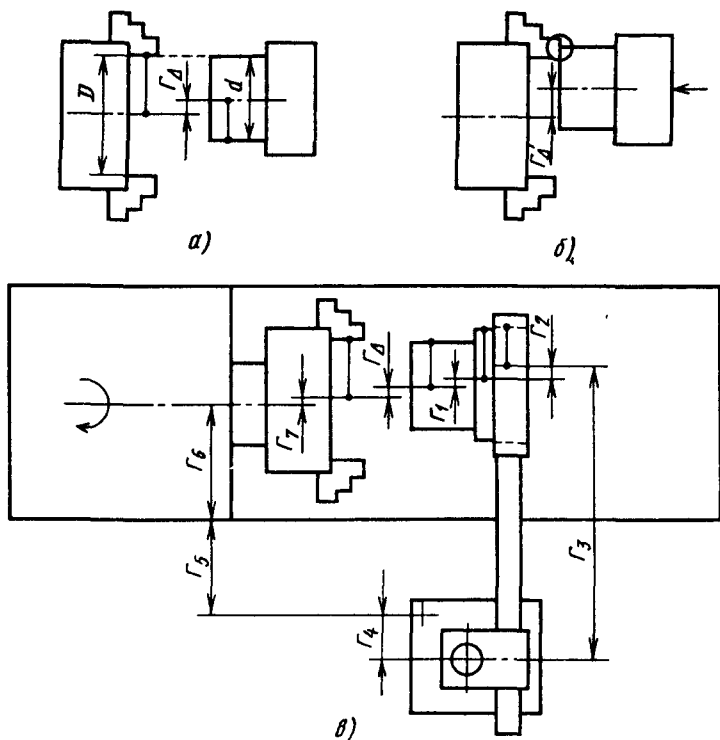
Схема размерных связей при автоматической загрузке станка
